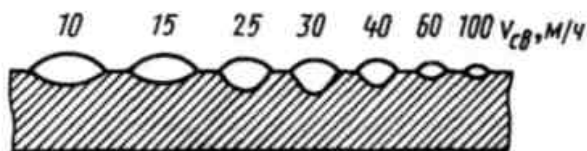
Вплив швидкості зварювання на форму шва.
